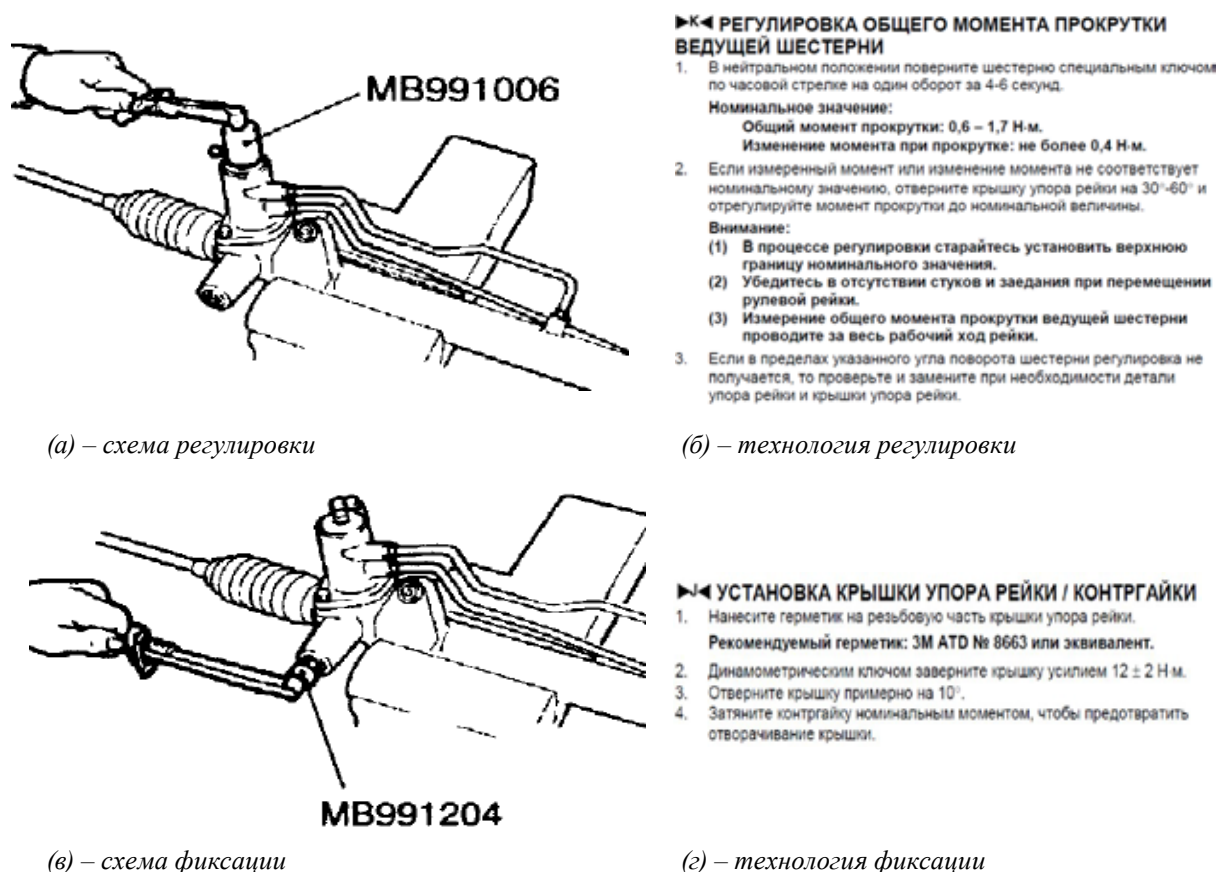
Регулировка общего момента прокрутки ведущей шестерни и положения упора рейки
